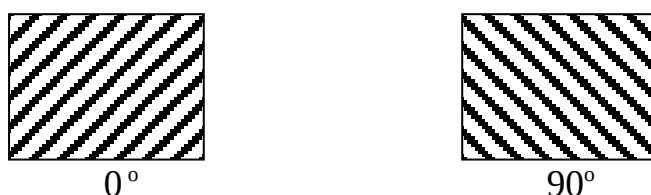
Угол наклона штриховки (материал детали - металл)
